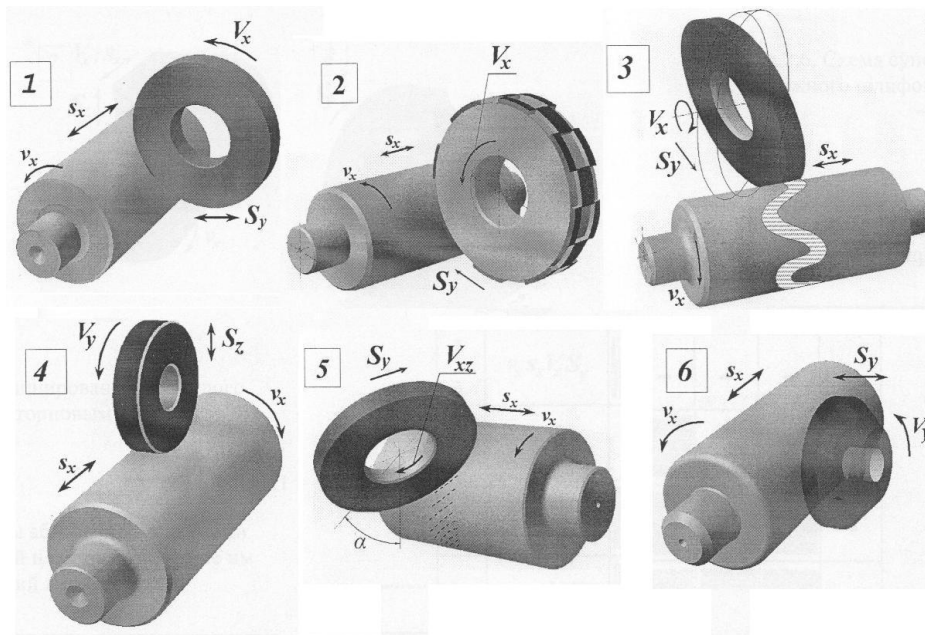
Схемы круглого наружного шлифования деталей цилиндрической формы
